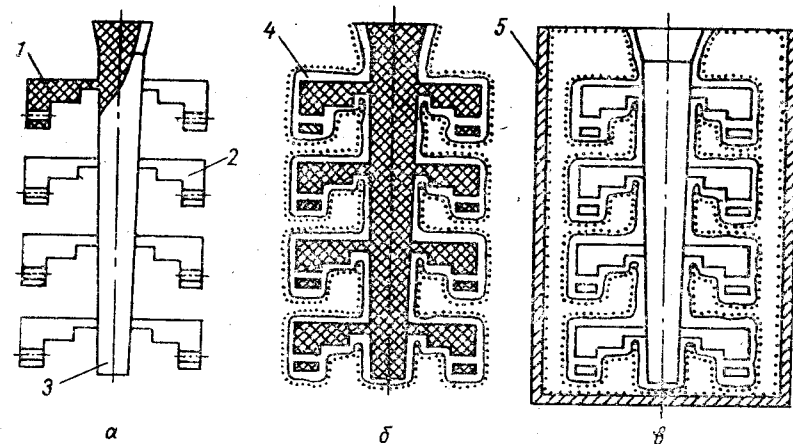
Схема виготовлення форми за витопними моделями:
